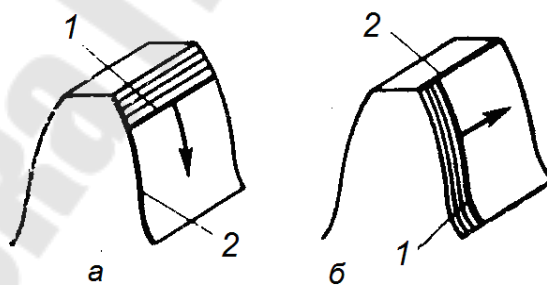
Схемы обработки боковой поверхности зуба прямозубого колеса
